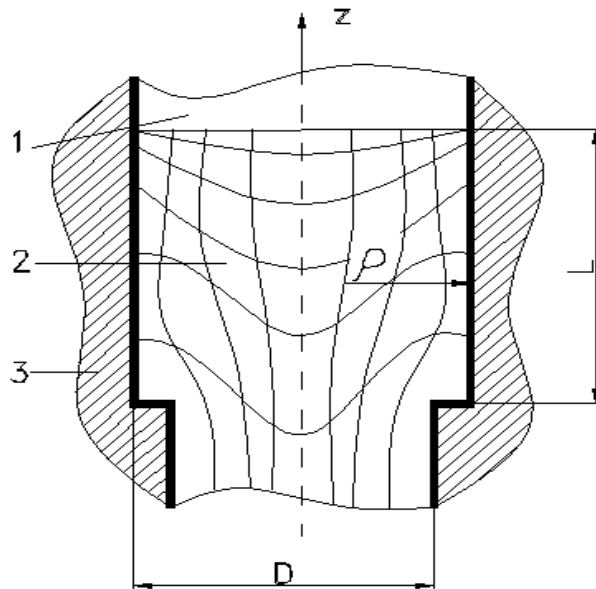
Цилиндрический приемник: 1 – плунжер; 2 – заготовка; 3 – матрица
